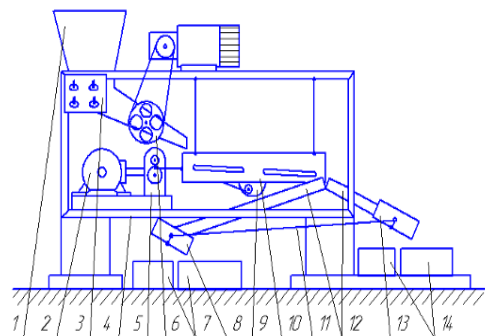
Схема лабораторной установки: 1 – бункер для исходной зерновой смеси; 2 – двигатель привода решета; 3 – пульт управления; 4 – рама; 5 – распределительный редуктор; 6 – привод дозатора зерна; 7 – емкости для сбора проходовой фракции; 8, 13 – клапаны; 9 – привод щеток; 10 – решетный стан; 11 – рычаг блокировки клапанов; 12 – лотки для сбора фракций; 14 – емкости для сбора сходовой фракции.
